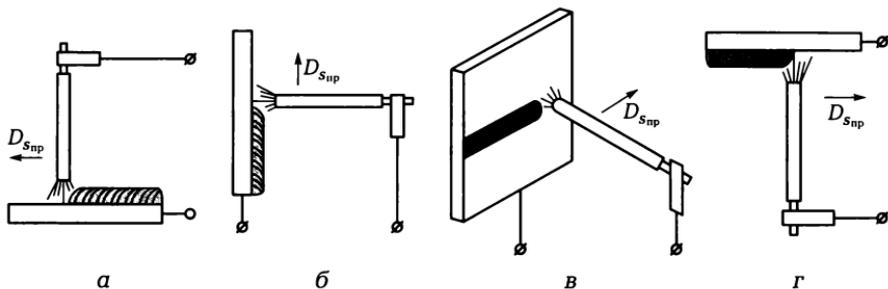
Возможные пространственные положения шва при ручной дуговой сварке:
